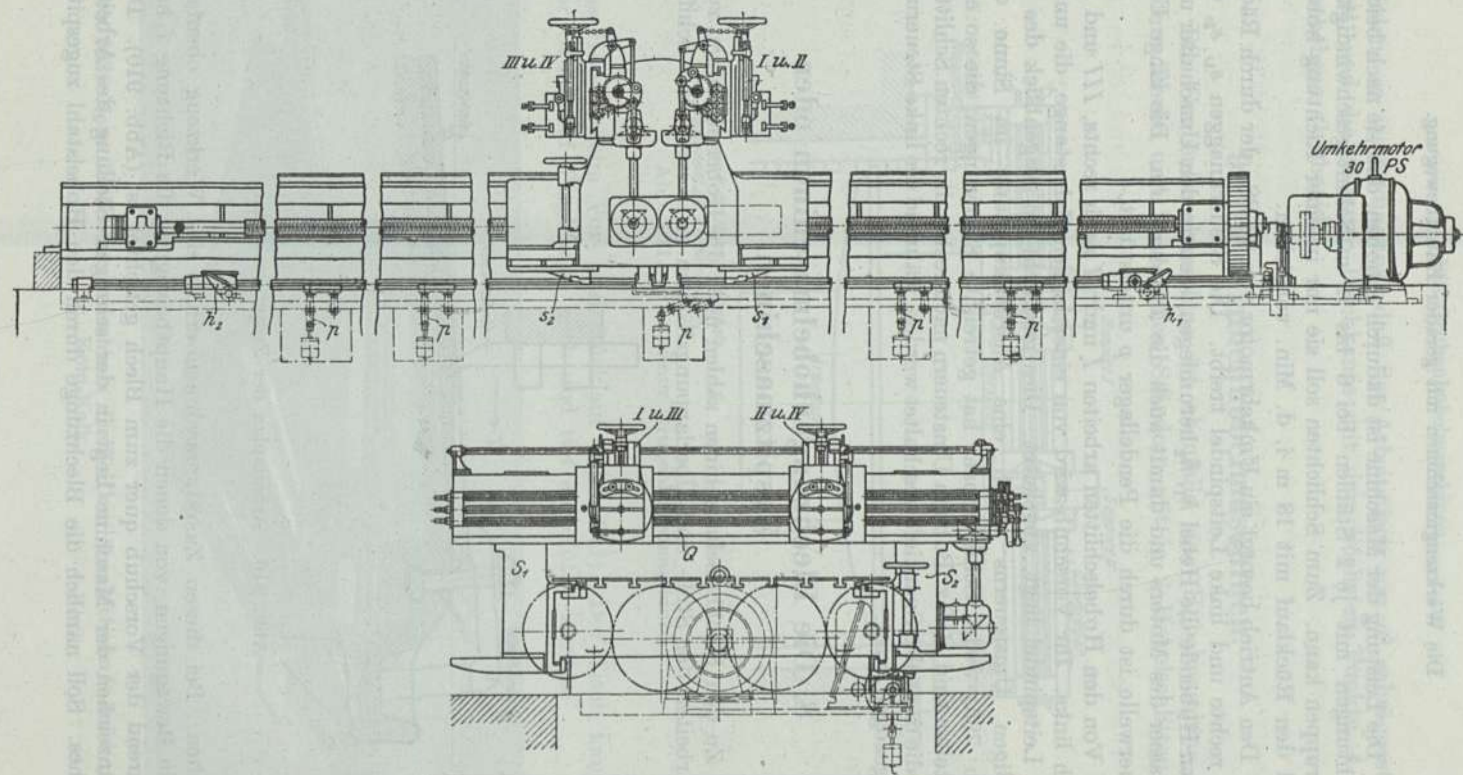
und 909. Blechkantenhobelmaschine mit 4 Werkzeugschlitzen. Wagner & Co., G. m. b. H., Dortmund.
